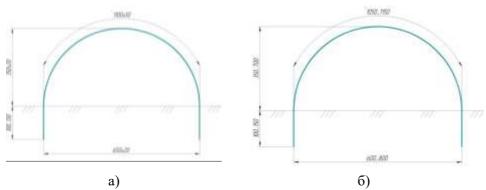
а) Оптимальный вид дуги для прутка длиной 1400 мм. б) Возможный вид дуги
